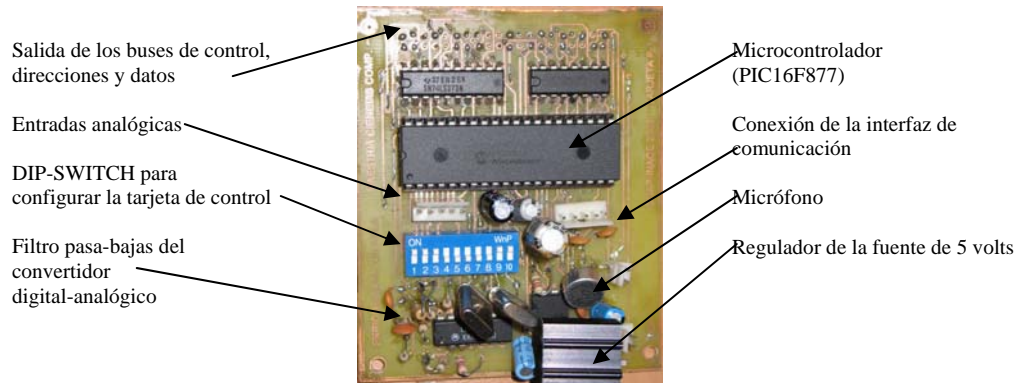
Ensamble físico de la primera parte de la tarjeta de control.
